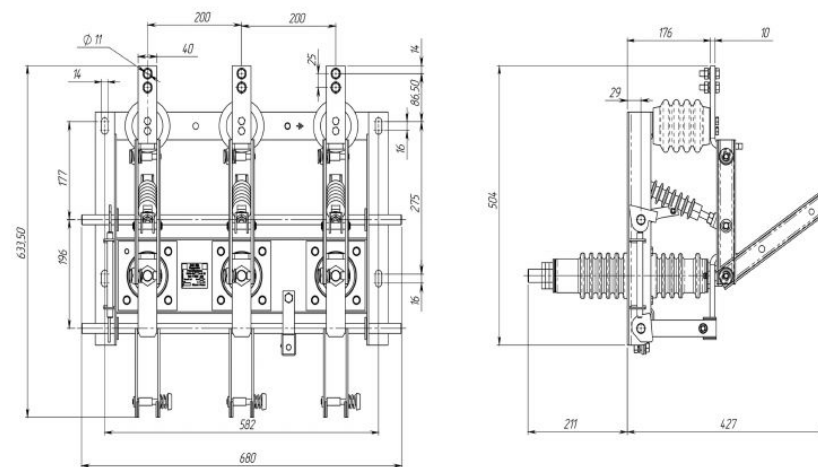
Разъединитель внутренней установки типа РВФЗ-10/1000-II-У2 с заземляющими ножами со стороны шарнирных контактов, масса не более 39 кг
